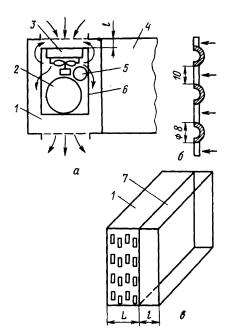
Схема установки экрана: а — схема циркуляции воздуха; б — решетки; в — установка экрана: 1 — машинное отделение; 2 — компрессор; 3 — конденсатор; 4 — охлаждаемый объем; 5 — ресивер; 6 — рама агрегата; 7 — экран
